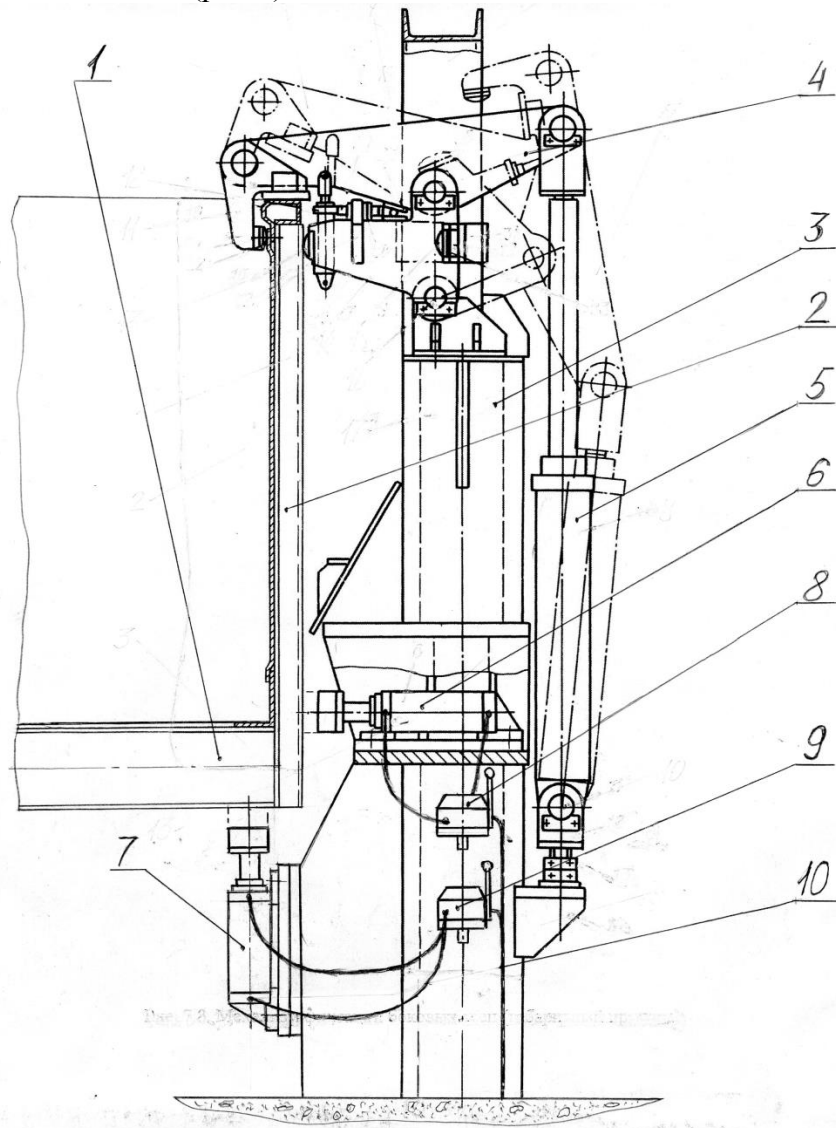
Колонна установки боковой стены стенда сборки кузова полувагона: 1 - балка рамы полувагона; 2 – боковая стена полувагона; 3 – колонна установки боковой стены; 4 – прижим габаритный для установки боковой стены; 5 – гидроцилиндр прижима габаритного; 6 – прижим горизонтальный; 7 – прижим вертикальный; 8 и 9 – дополнительные гидрораспределители с ручным управлением для управления соответственно горизонтальным 6 и вертикальным 7 прижимами; 10 – основная гидросистема стенда сборки кузова полувагона
